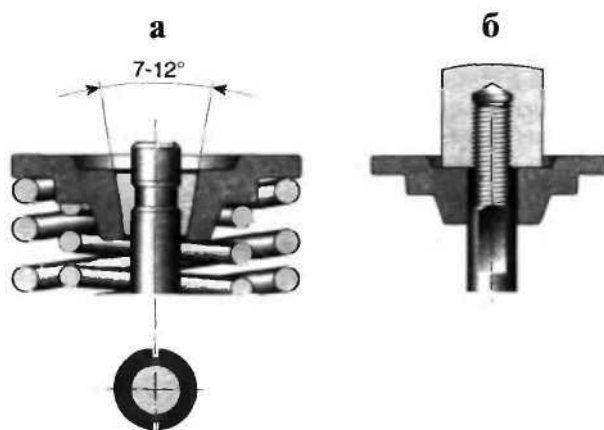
Кріплення тарілки пружини на стержні клапана: а - за допомогою сухарів; б – гайкою
